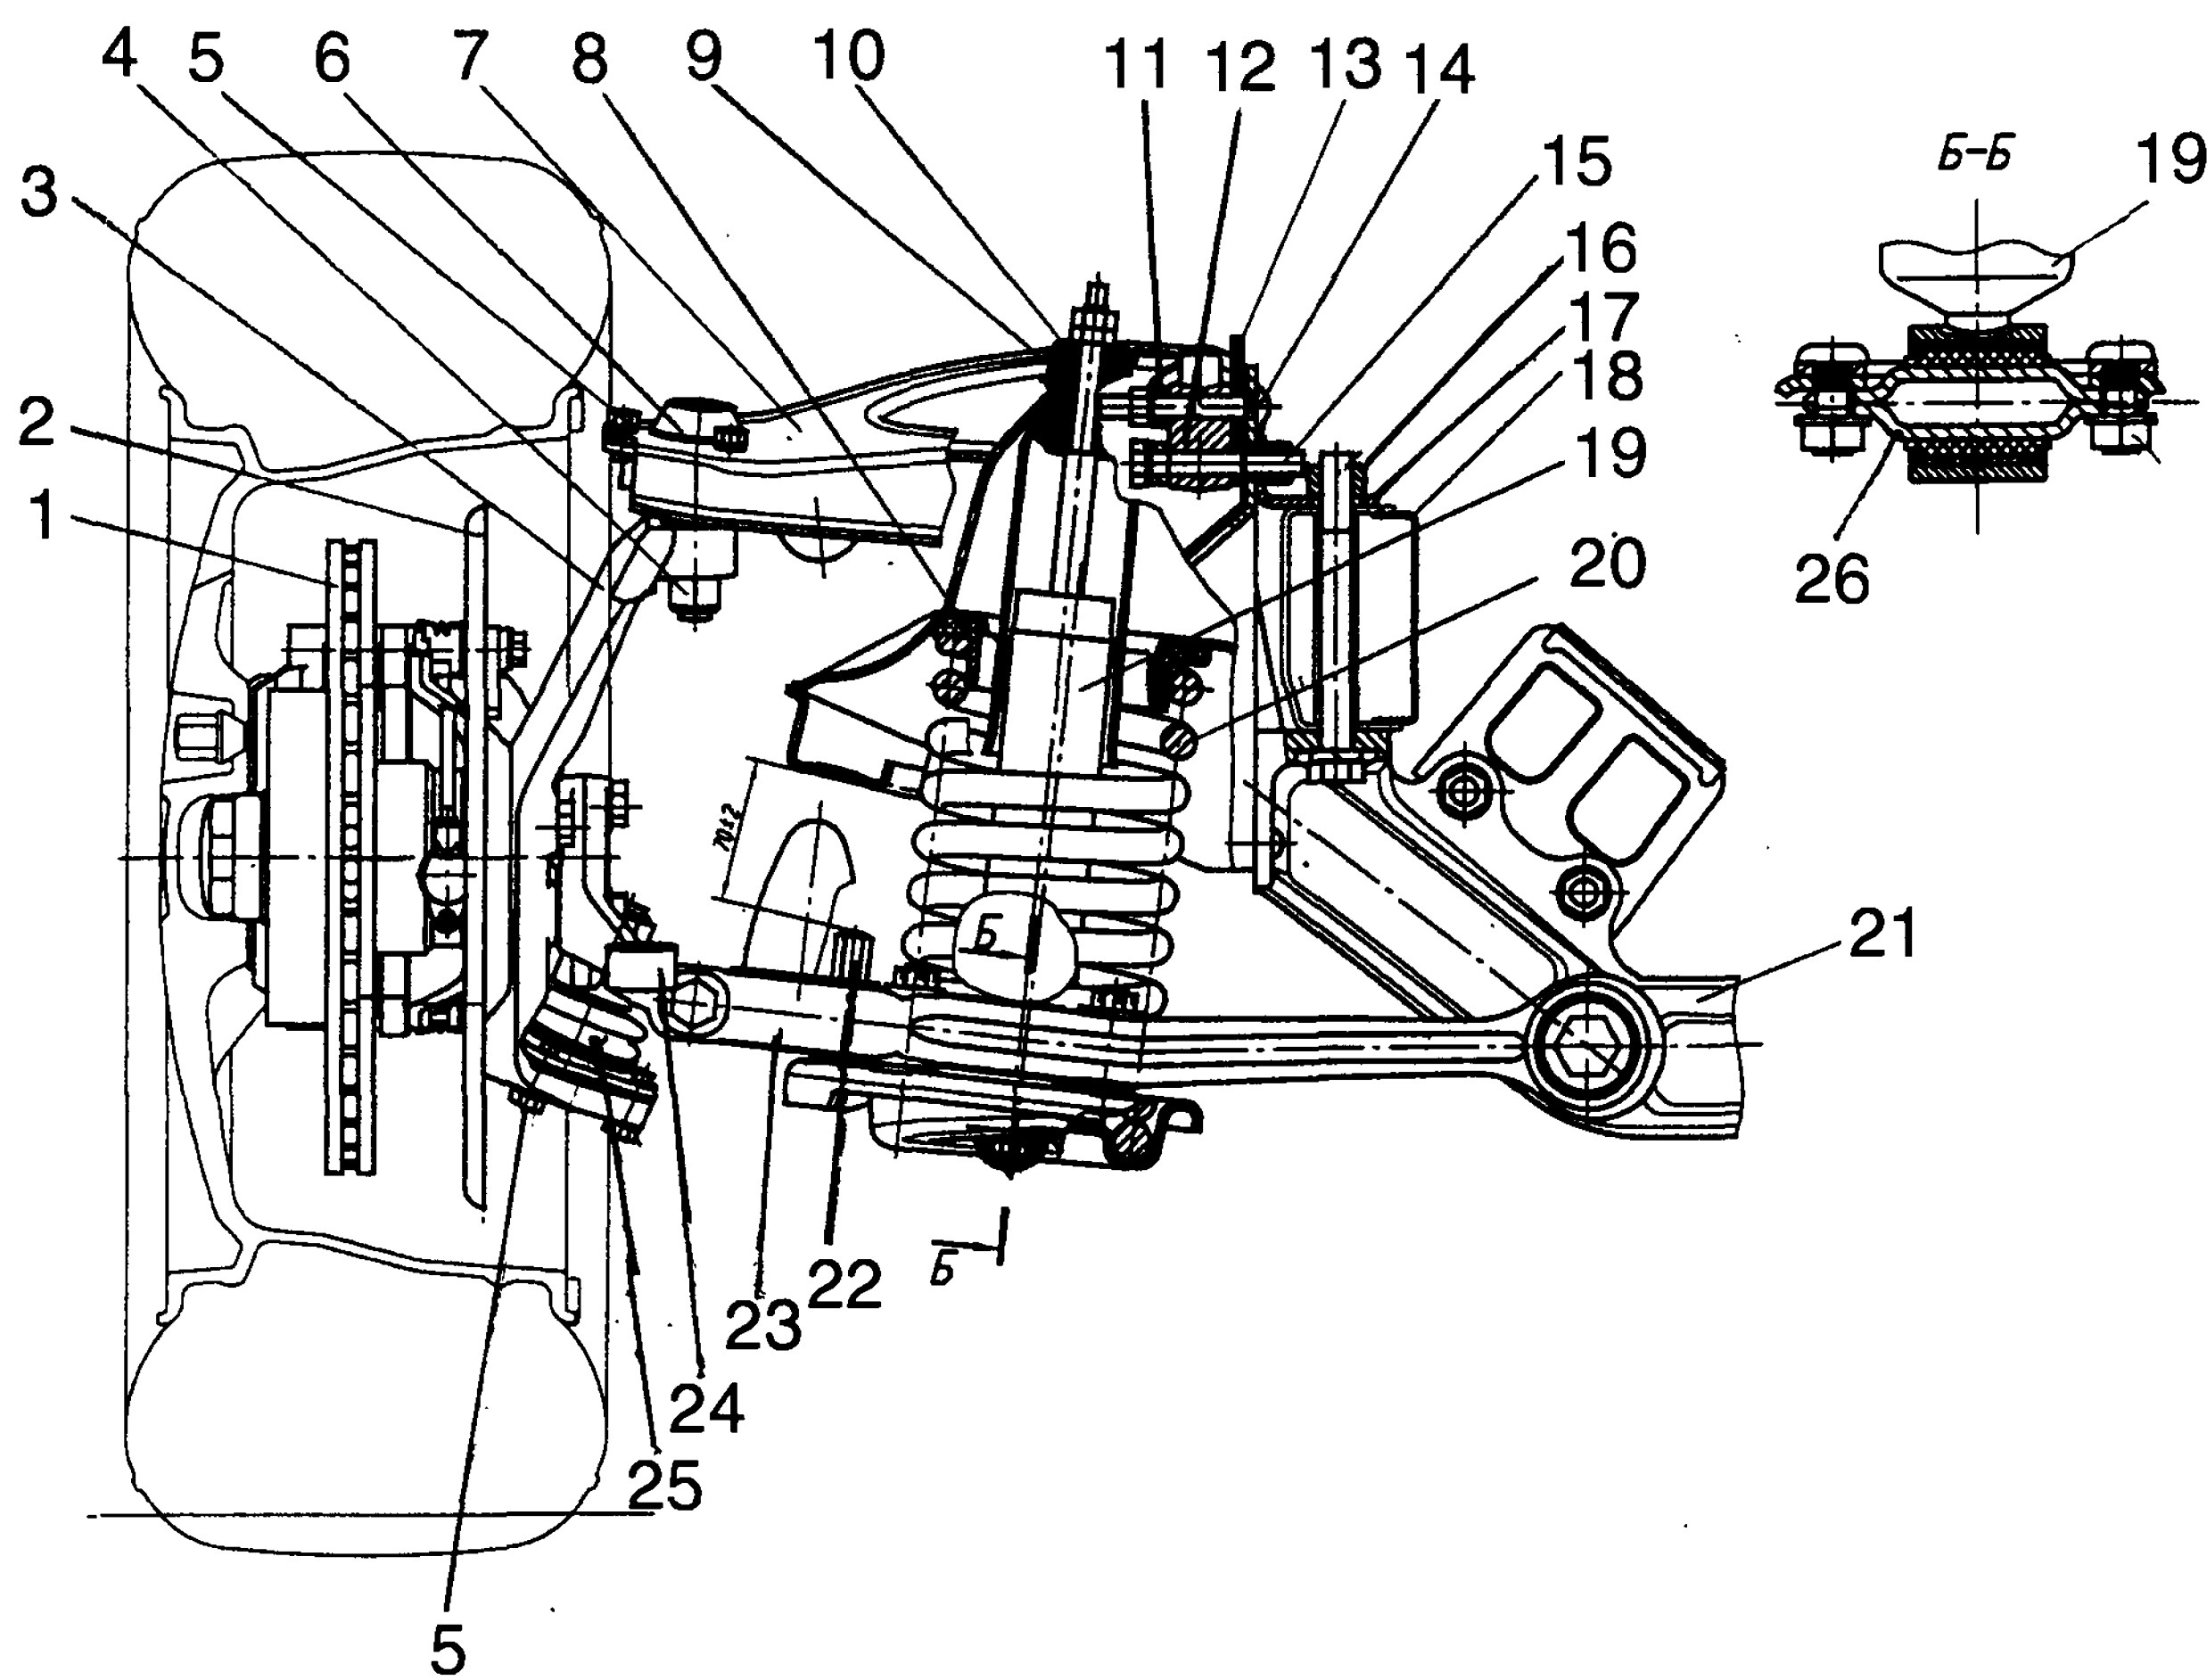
Подвеска передняя: 1 - тормозной диск; 2 - тормозной щит; 3 - стойка; 4 - гайка пальца шарового шарнира; 5 - болты крепления шарнира; 6 - верхний шаровой шарнир; 7 - верхний рычаг; 8 - прокладка пружины; 9 - подушка амортизатора; 10 - чашка подушки; 11 - втулка дистанционная; 12 - ось верхних рычагов; 13 - регулировочные прокладки; 14 - болт крепления оси верхних рычагов; 15 - планка горизонтального крепления; 16 - планка вертикального крепления; 17 - кронштейн крепления подвески к лонжерону; 18 - лонжерон; 19 - амортизатор; 20 - пружина; 21 - поперечина (балка); 22 - болт-ограничитель хода сжатия; 23 - нижний рычаг; 24 - рычаг поворотный; 25 - нижний шаровой шарнир; 26 - шарнир амортизатора
